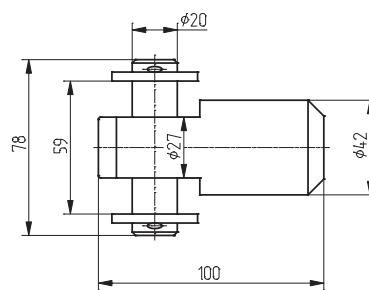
Соединительная тяга для механизмов МЗО-1600-92К (КБ) (в комплекте - вилка и шток)
